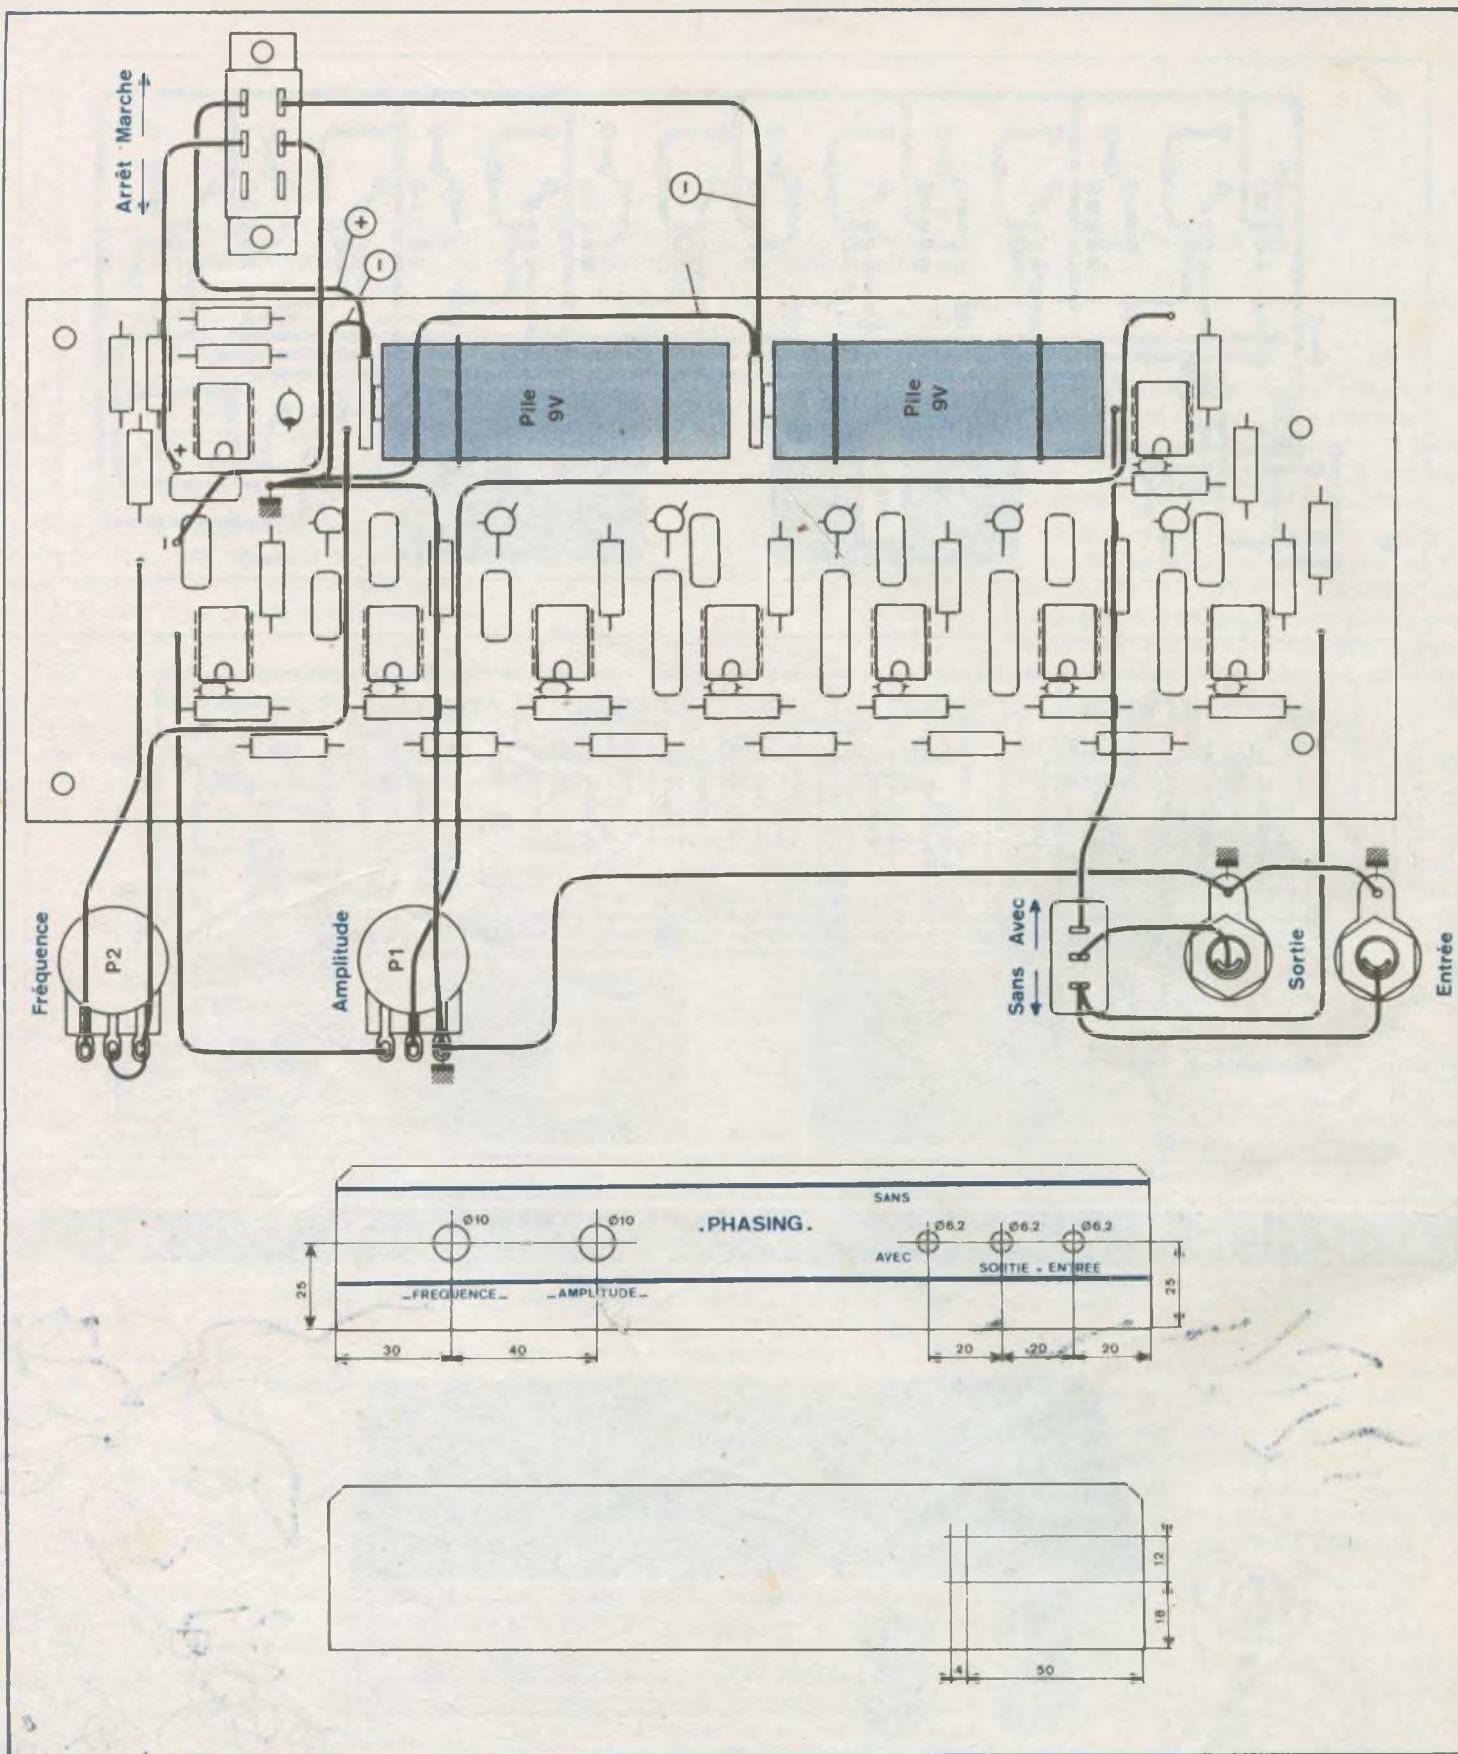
et 4. — Le montage réclame 18 V de tension d'alimentation aussi la place des deux piles miniatures a-t-elle été réservée. Plan de câblage vers les éléments extérieurs. A l'échelle 1/2 nous proposons un dessin de face avant et un plan de perçage.
